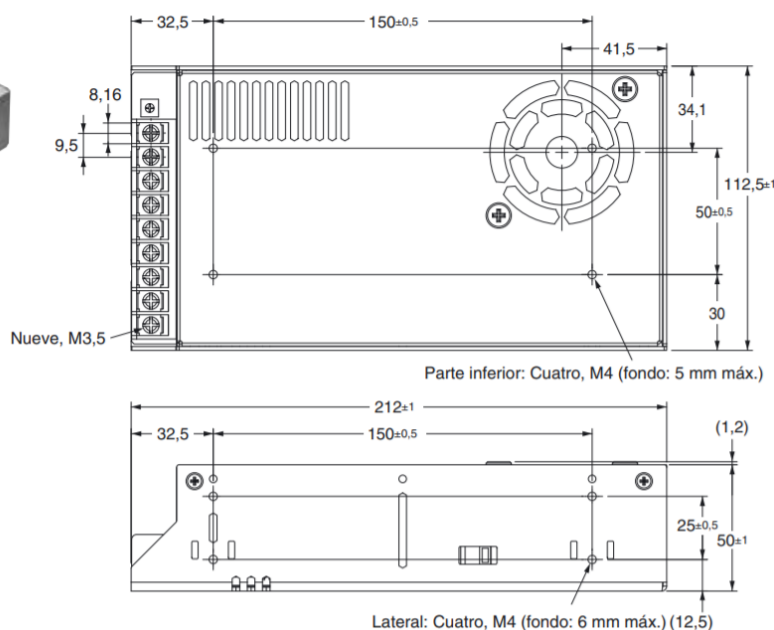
Dimensiones fuente switching. Fuente: Omron (2015).
